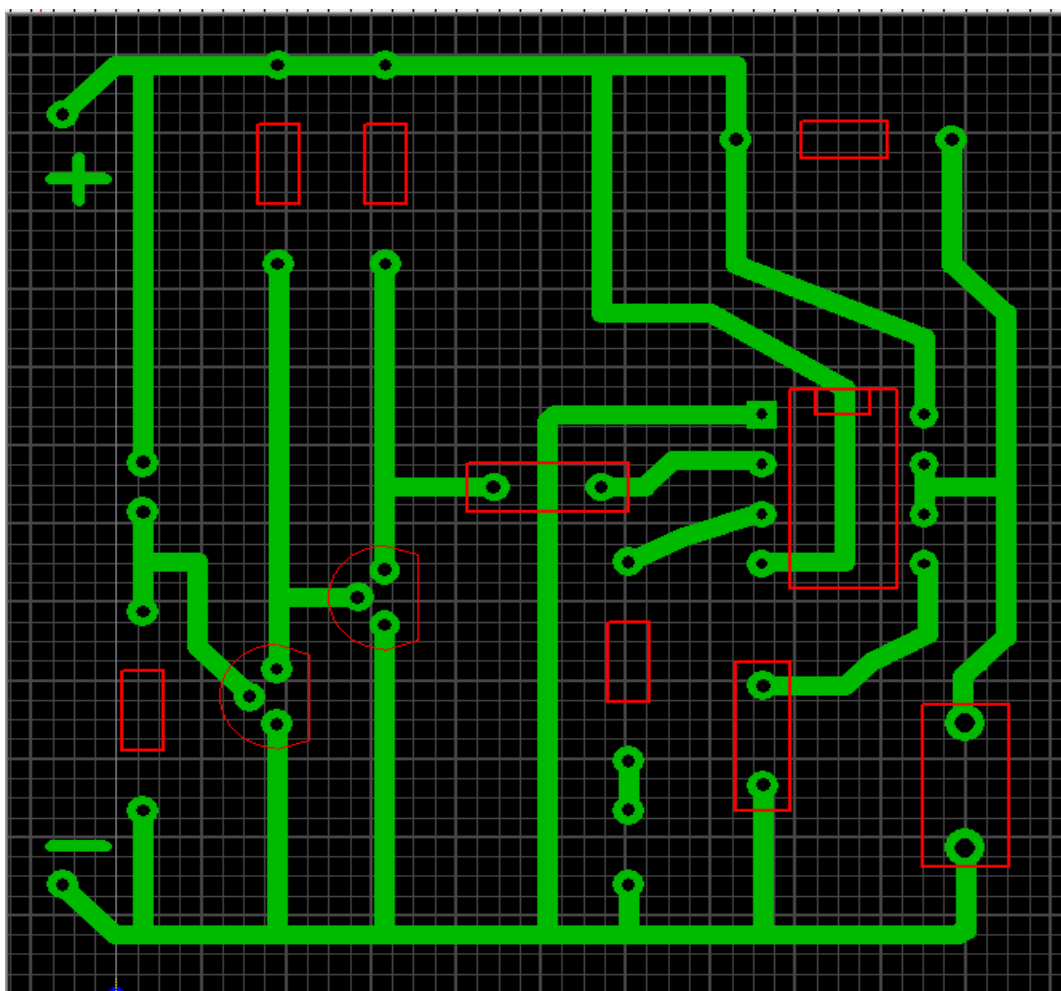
Креслення плати в Sprint Layout 6.0.
